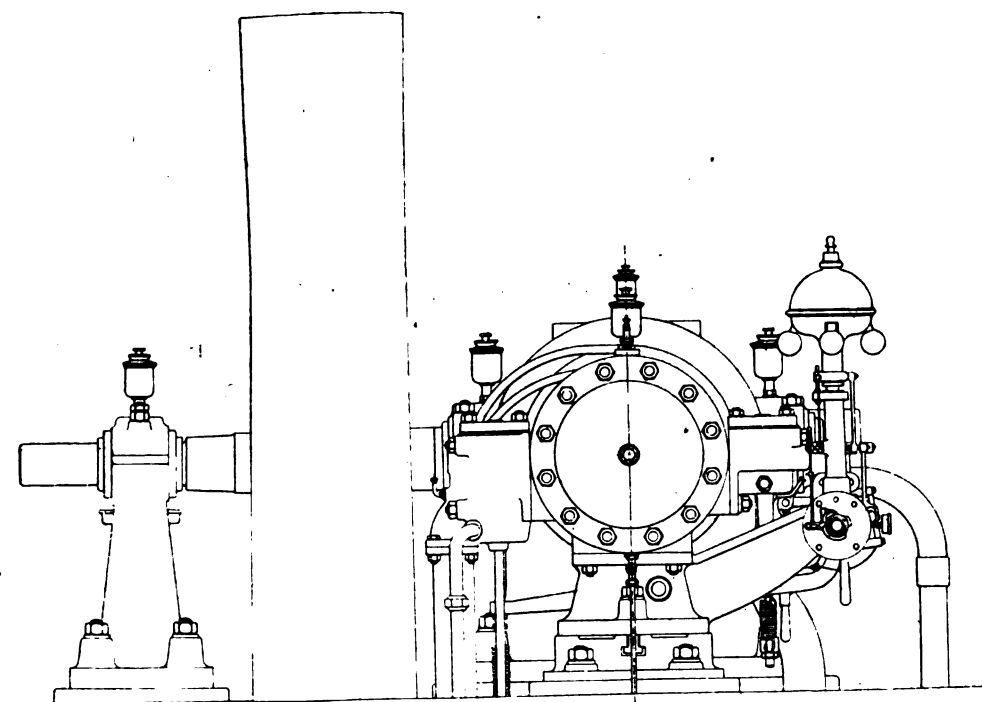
Vue arrière d'un moteur à soupapes opposées.
